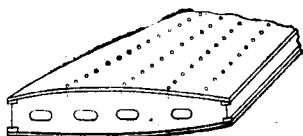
Крепление одной из обшивок в агрегатах оперения.
